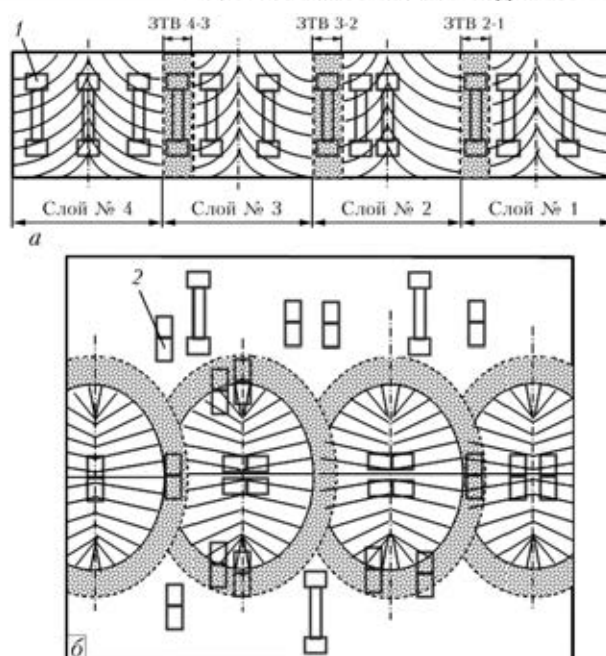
Схема вырезки образцов для проведения механических испытаний сварных соединений, выполненных МЭШС: а — продольный; б — поперечный темплет многослойного электрошлакового шва; 1, 2 — образцы для испытаний на статическое растяжение («гагаринские») и ударный изгиб («менаже») соответственно
